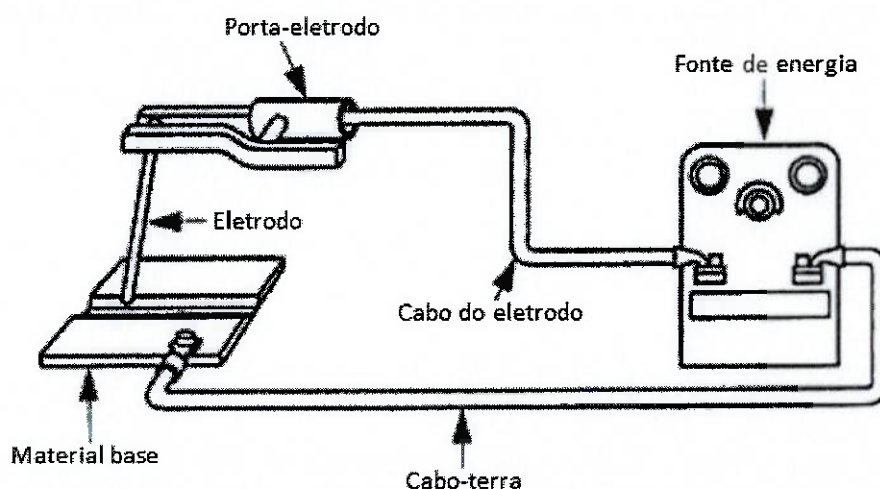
Equipamento básico para soldagem com eletrodo revestido [6].
